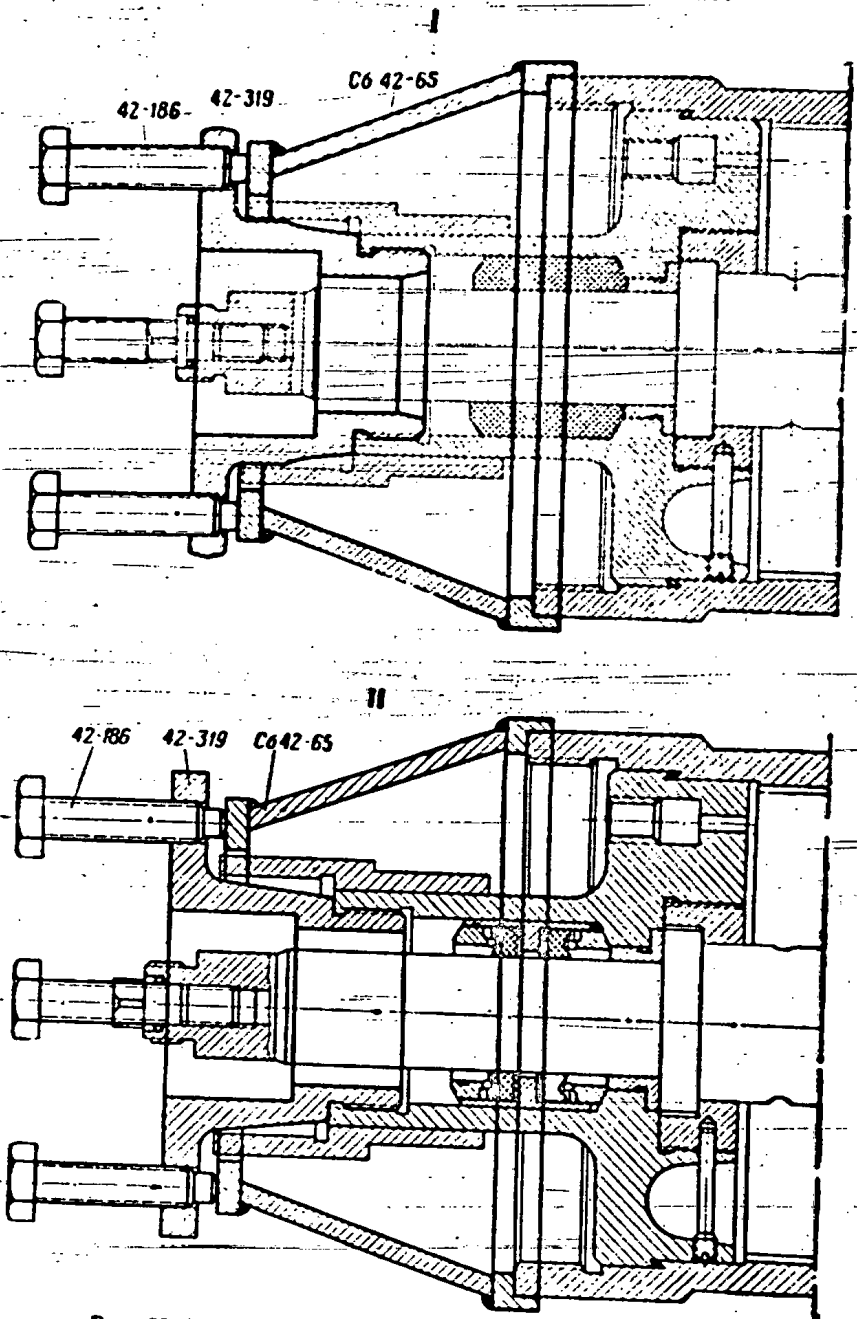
Прибор для разборки тормоза отката (C642-45):
